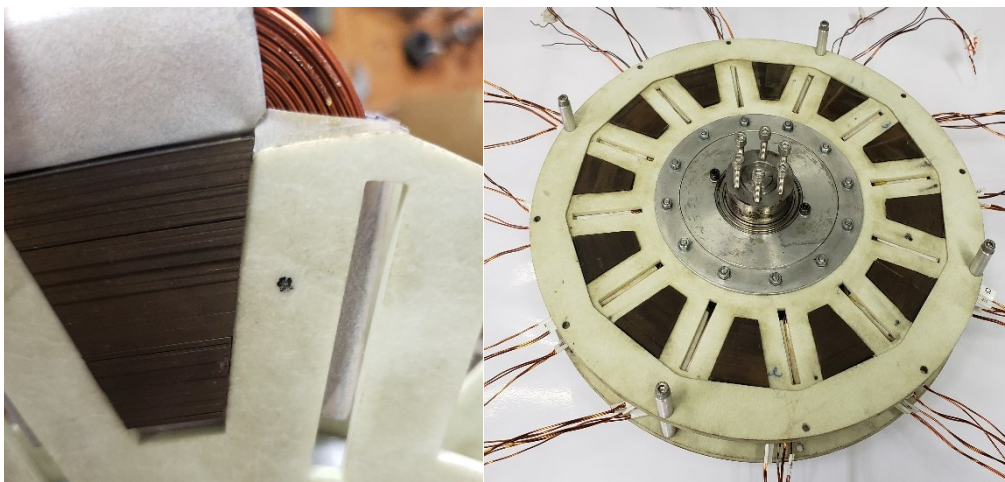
Processo de bobinagem de um polo do estator com suporte.
